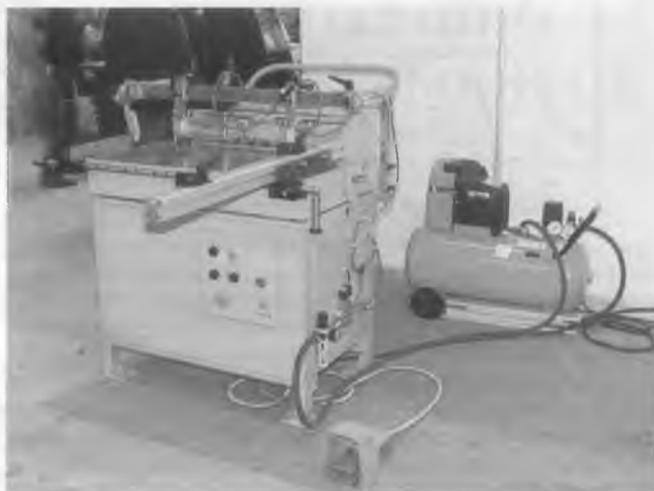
Общий вид сверлильно-присадочного станка СС-21
